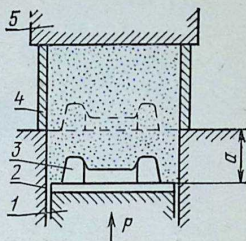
Схема формовочной машины с нижним уплотнением формовочной смеси:
